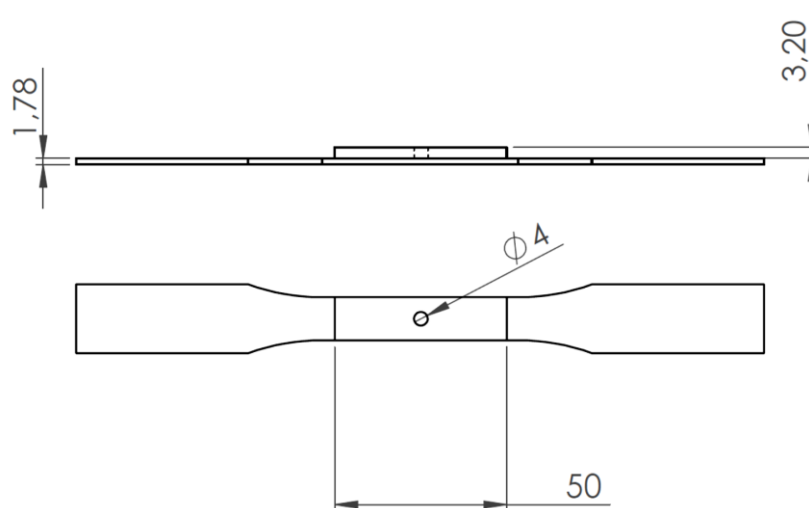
Desenho com as dimensões do corpo de prova, medidas em mm.
